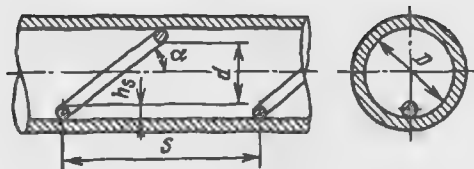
Общий вид трубы со спирально-винтовыми проволочными вставками
